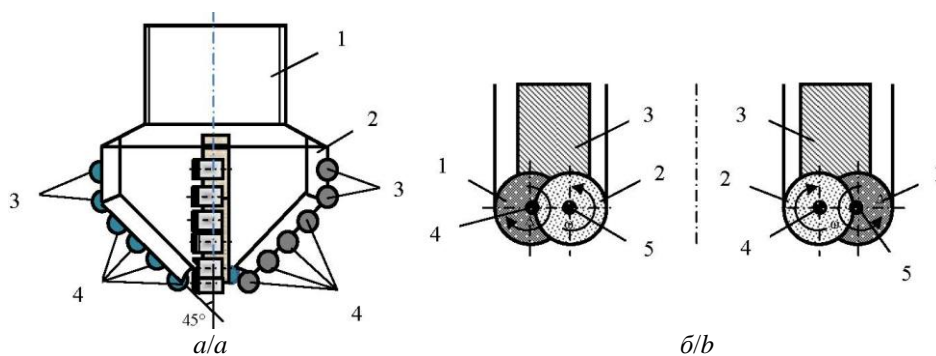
Породоразрушающий инструмент с вращающимися при бурении резцами типа PDC: а) буровое долото: 1 – корпус с резьбой; 2 – матрица; 3 и 4 – вращающиеся резцы; б) буровая коронка: 1 – наружный скважинообразующий резец; 2 – внутренний кernoобразующий резец; 3 – матрица коронки; 4 – ось вращения наружных скважинообразующих резцов; 5 – ось вращения внутренних кernoобразующих резцов; 6 – элементы каркаса осей вращения резцов
